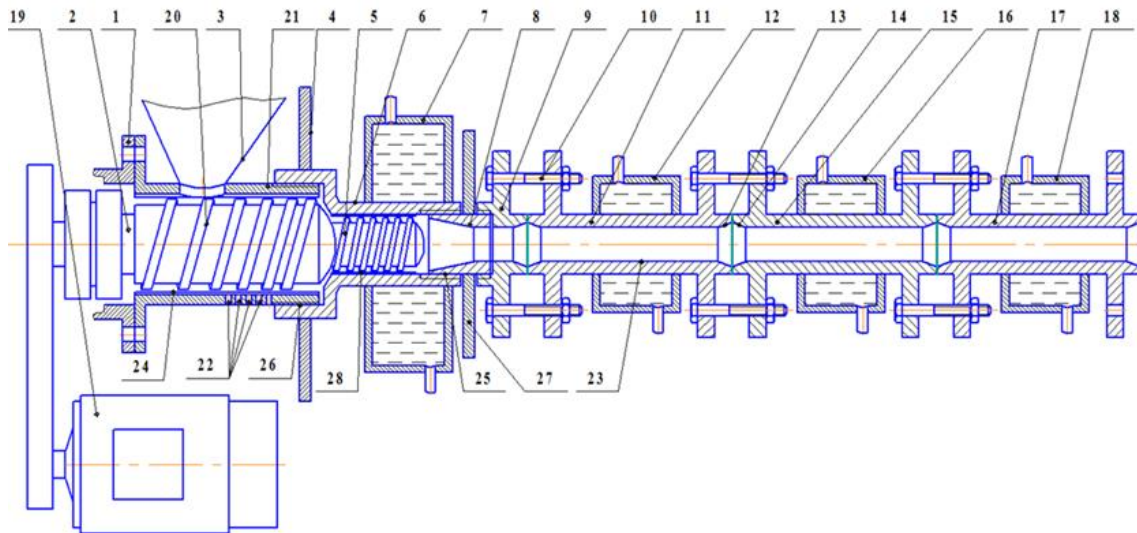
Схема шнекового прес-екструдера для отримання паливних брикетів з пристроєм остаточного формування: 1 – підшипниковий вузол; 2 – вал приводу; 3 – бункер; 4 – фіксатор; 5, 20 – шнек; 6 – камера дожиму; 7, 12, 16, 18 – сорочка охолодження; 8 – матриця; 9 – пристрій остаточного формування; 10 – болт; 11, 15, 17 – секції труб; 13, 14 – масло згінні фаски; 19 – електродвигун; 21 – пресуюча камера; 22 – отвори для відводу масла; 23 – труба; 24, 28 внутрішні ребра; 25, 26 – різьбове з’єднання; 27 – рукоятка
